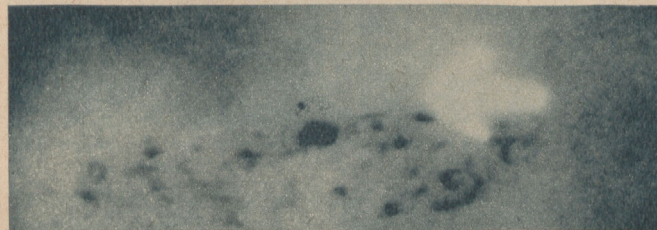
Zurückgebliebene Fehlstellen in einer Flickschweißung (Kesseltrommel). Die Aufhellung (Pfeil) stammt von einer Bleimarke, die zur Kennzeichnung auf die Naht gelegt wurde
